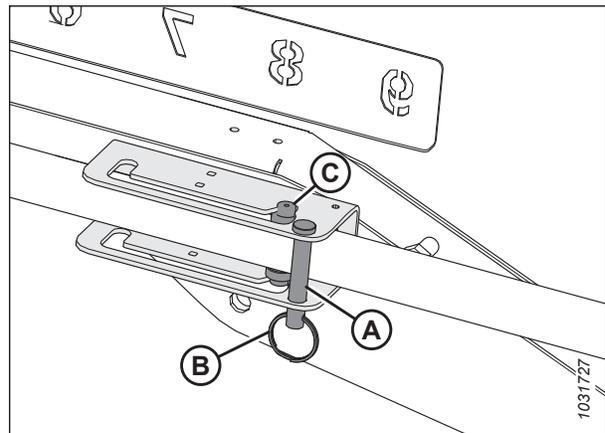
Cilindro del braccio esterno sinistro – Posizione arretrata
